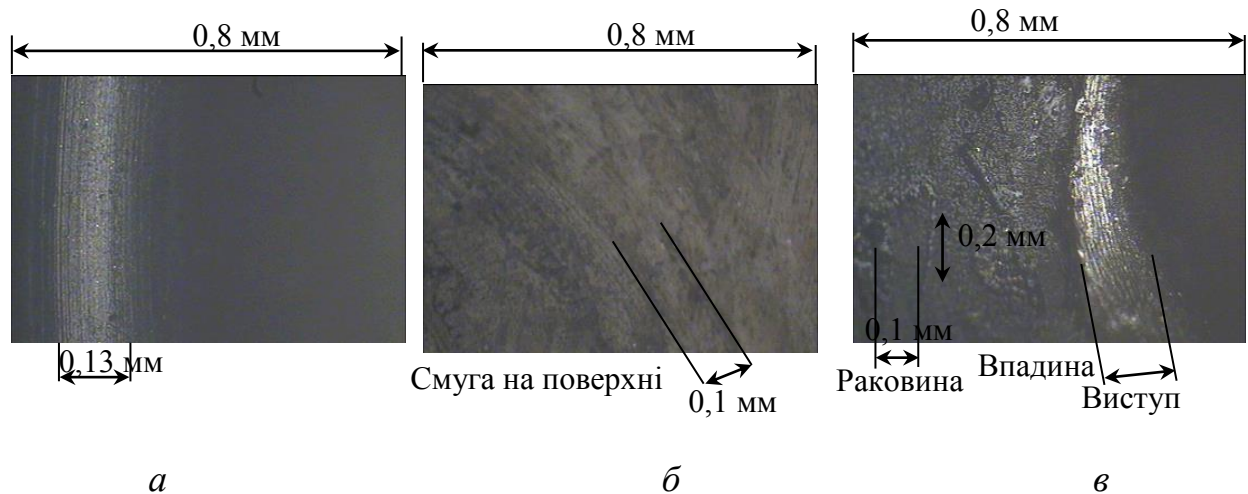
Окремі дефекти на гумовій поверхні нового клапана: *a* – сліди токарної обробки; *б* – смуги на гумовій поверхні; *в* - локальні дефекти гумової поверхні, які виникають при порушенні технологічного процесу обробки гуми
